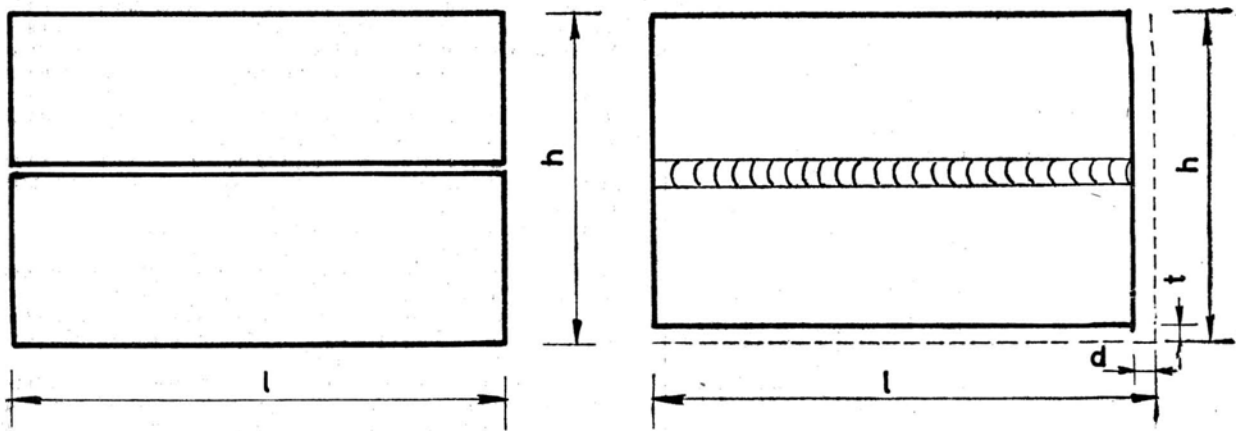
DEFORMACIONES LINEALES POR LA SOLDADURA
